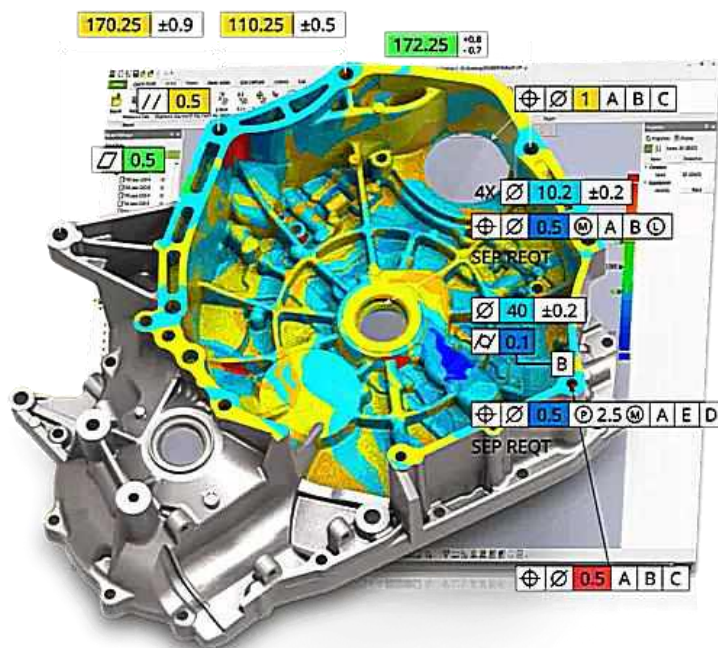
Комп'ютерна модель деталі з геометричними розмірами та допусками розташування
